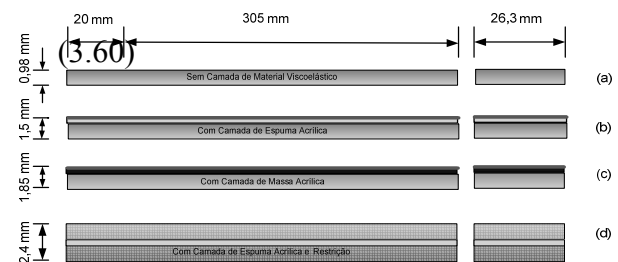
Dimensões das estruturas utilizadas nos ensaios
